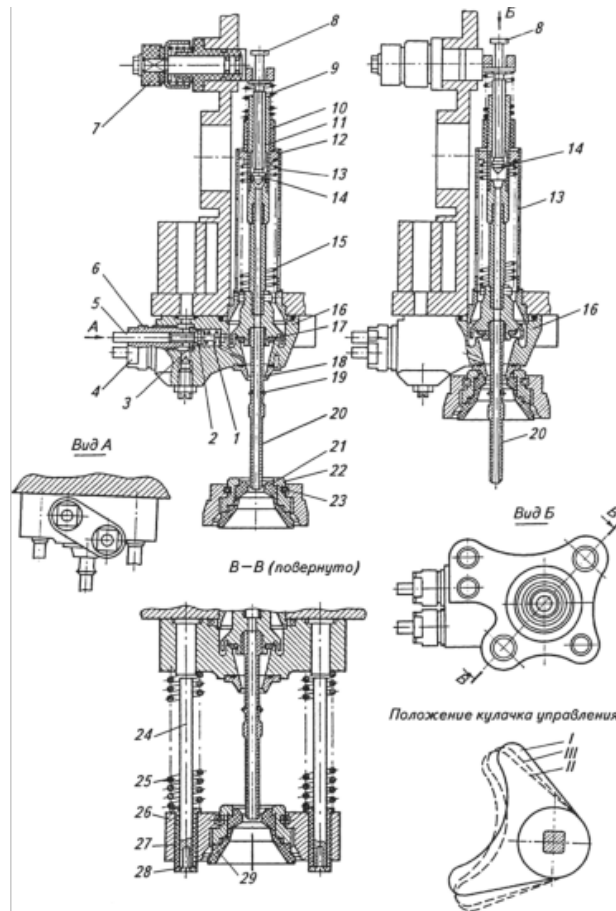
Фасувальний пристрій агрегату ВРМ / 1: 1, 9, 15, 25 - пружини; 2, 14 - ущільнювальні кільця; 3 - прокладка; 4 - корпус; 5 - вакуумний клапан; 6 - корпус вакуумного клапана; 7 - механізм кулачка; 8- голка газового клапана; 10, 12 - розпірна і спрямовуюча втулки; 11, 27 - втулки; 13 - кожух пружини рідинного клапана; 16 - корпус фасувальної частини; 17 - ущільнення; 18-конус; 19 - кільце; 20 - газова трубка; 21 - ущільнення; 22 - ущільнювач; 23 - затискна втулка; 24 - штанга; 26 - корпус центрувального дзвіночка; 28 - шайба; 29 - центрувальний дзвіночок; I, II, III - положення кулачка управління (I - газовий і рідинний клапани закриті; II- газовий і рідинний клапани відкриті; III - нейтральне)
